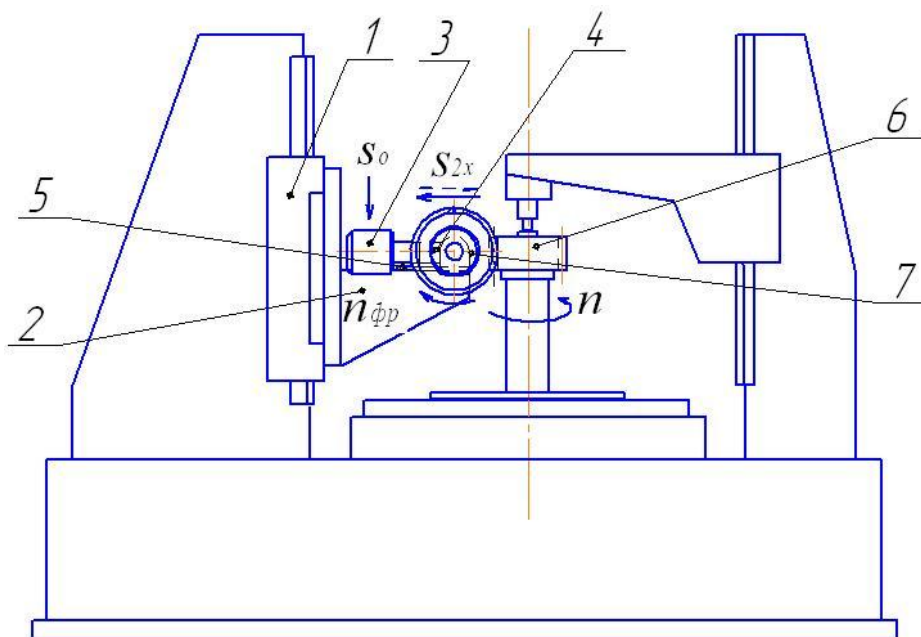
Будова зуборезного верстату з керованими приводами на основі РК-способу
